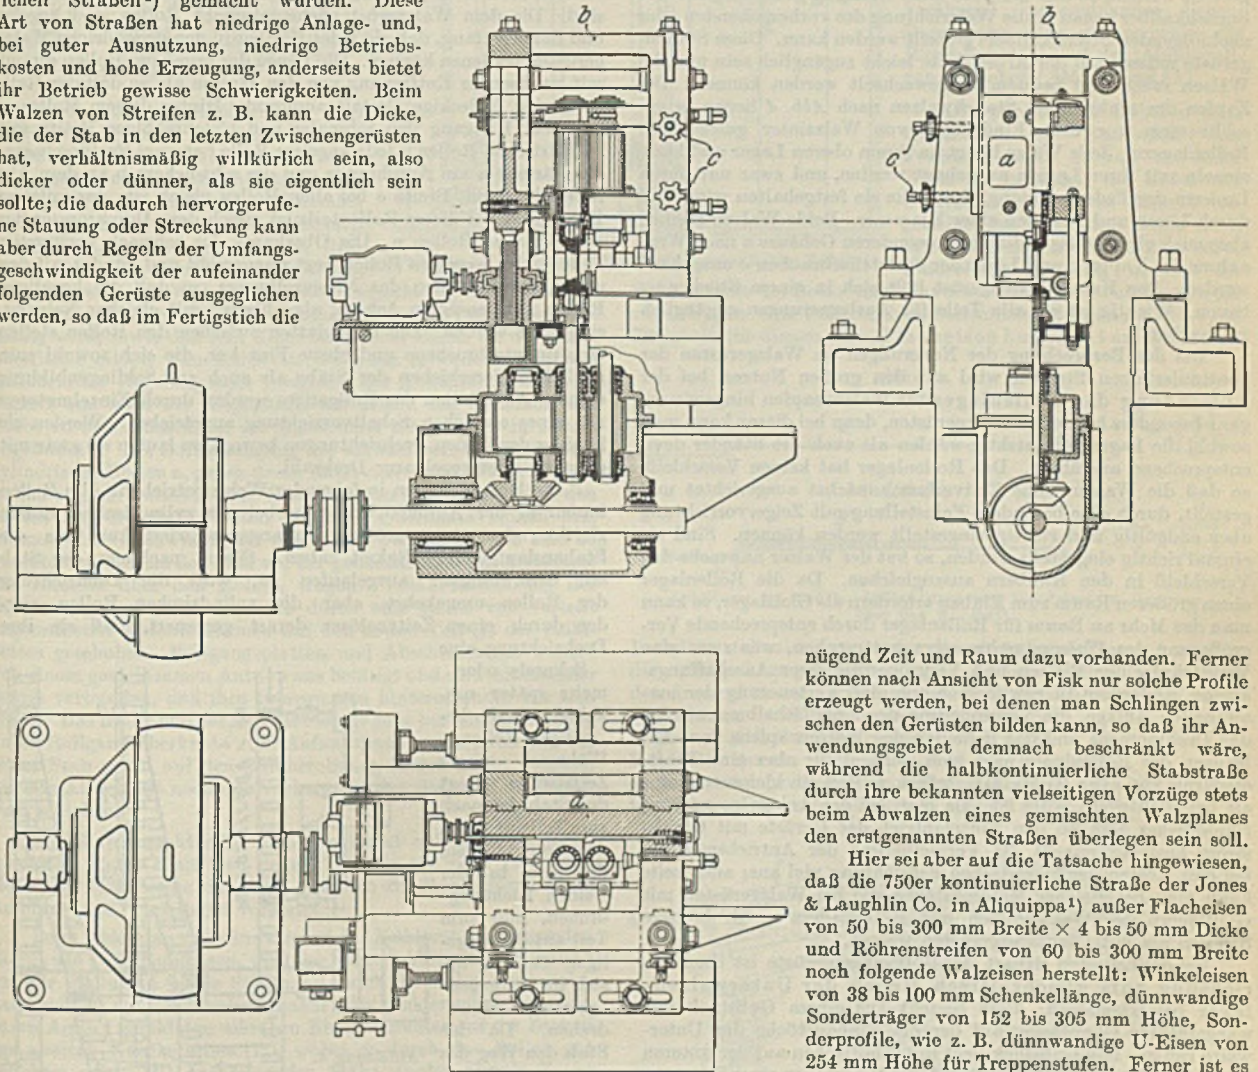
Gerüst mit senkrechten Stauchwalzen.
